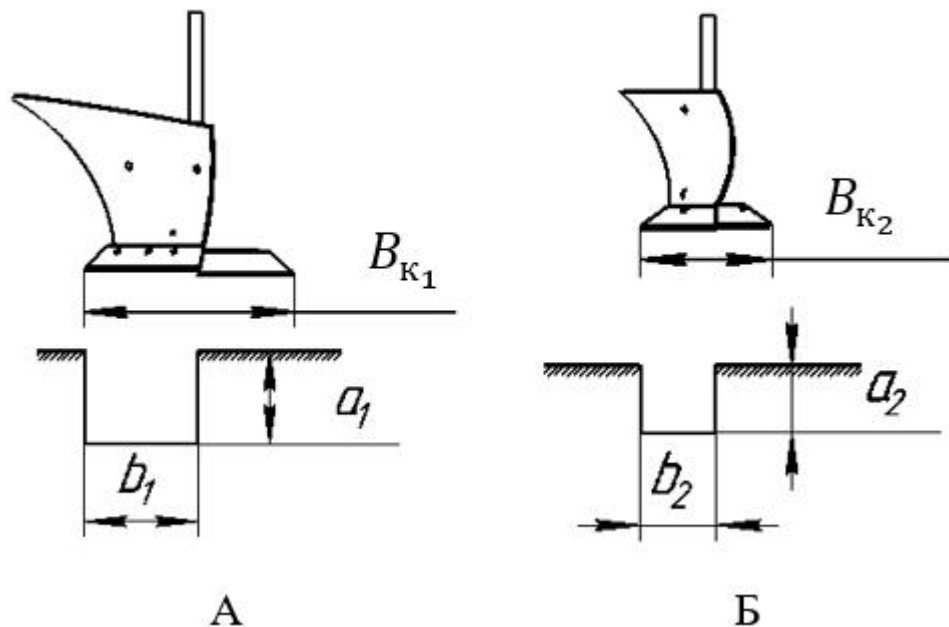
Корпус плуга и профиль борозды: А – комбинированный корпус плуга ПБС, Б – модернизированный корпус секционного плуга ПБС;  $B_{к}$  – ширина захвата корпуса;  $a$  – глубина борозды;  $b$  – ширина борозды
